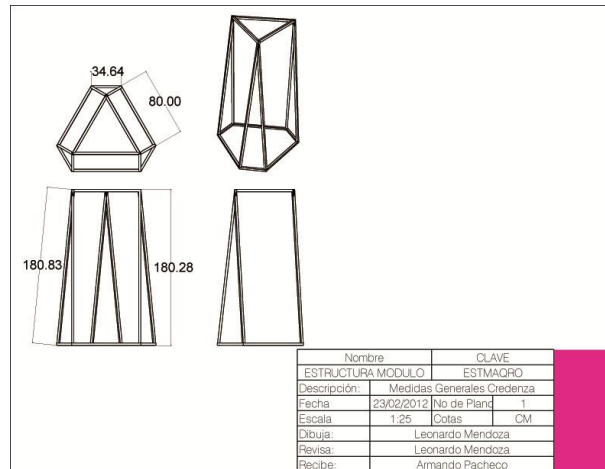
Planos del diseño original de la estructura del módulo para el sistema.
